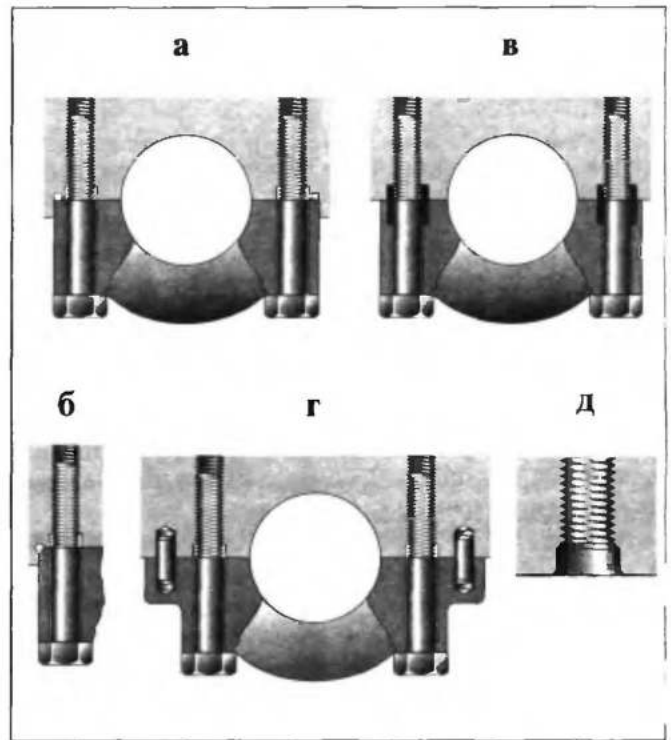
Способы крепления крышек коренных подшипников коленчатого вала к блок-картеру
